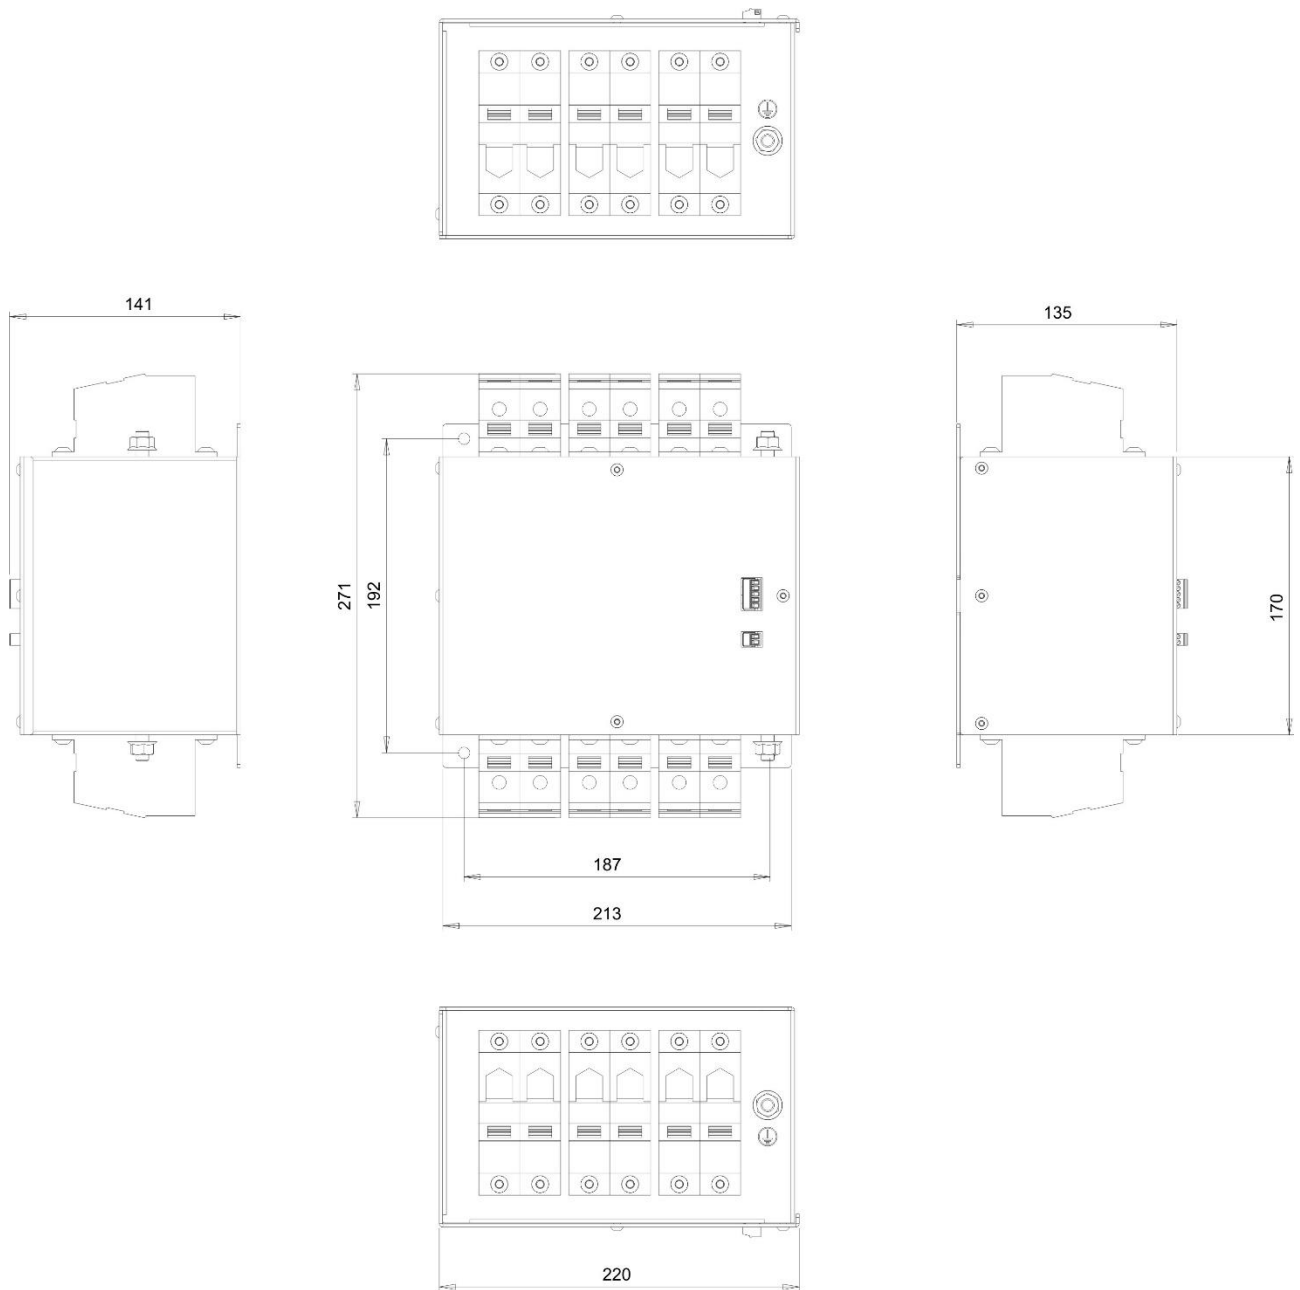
Dimensioni modulo sensori di corrente AFE Tless per OPDE S 220, 250
